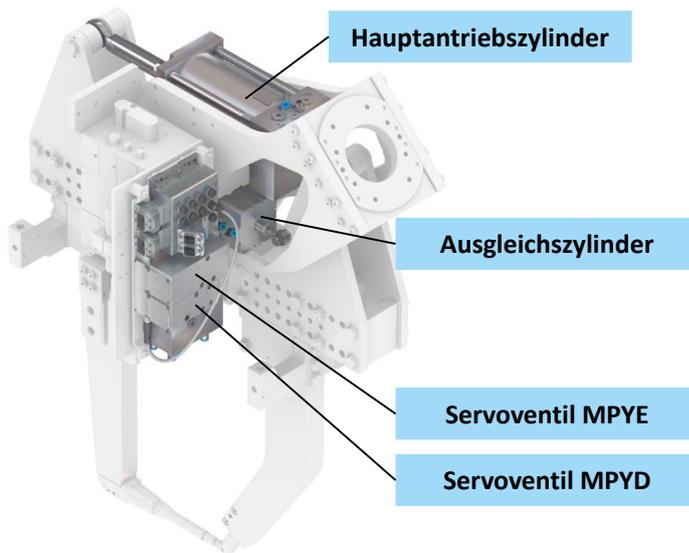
Servopneumatische Schweißzange mit den Hauptkomponenten [BLUM22, S. 376]
